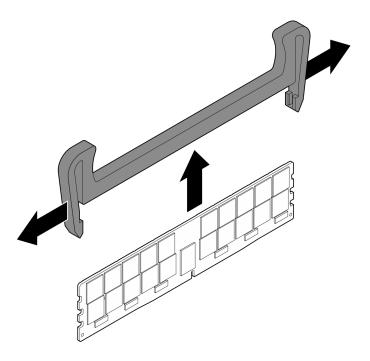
Entfernen des Werkzeugs zur DIMM-Entfernung aus dem DIMM
